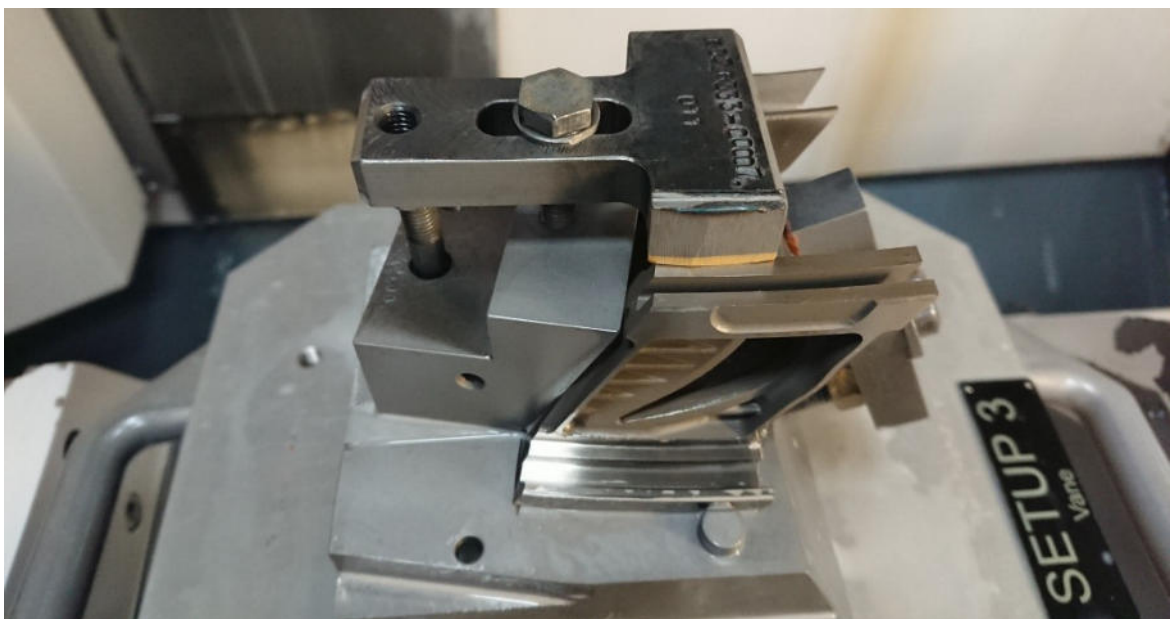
Приспособление для обработки сопловой лопатки, установленной на сменной паллете
